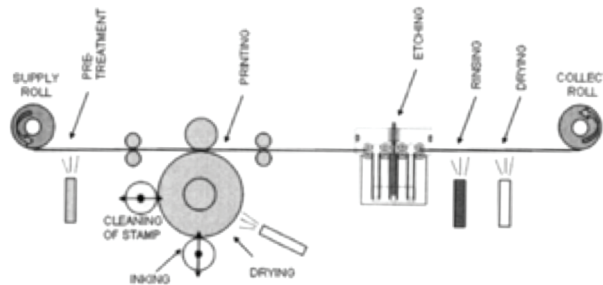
Machine de μ TP développée par le département d'ingénierie mécanique du MIT
